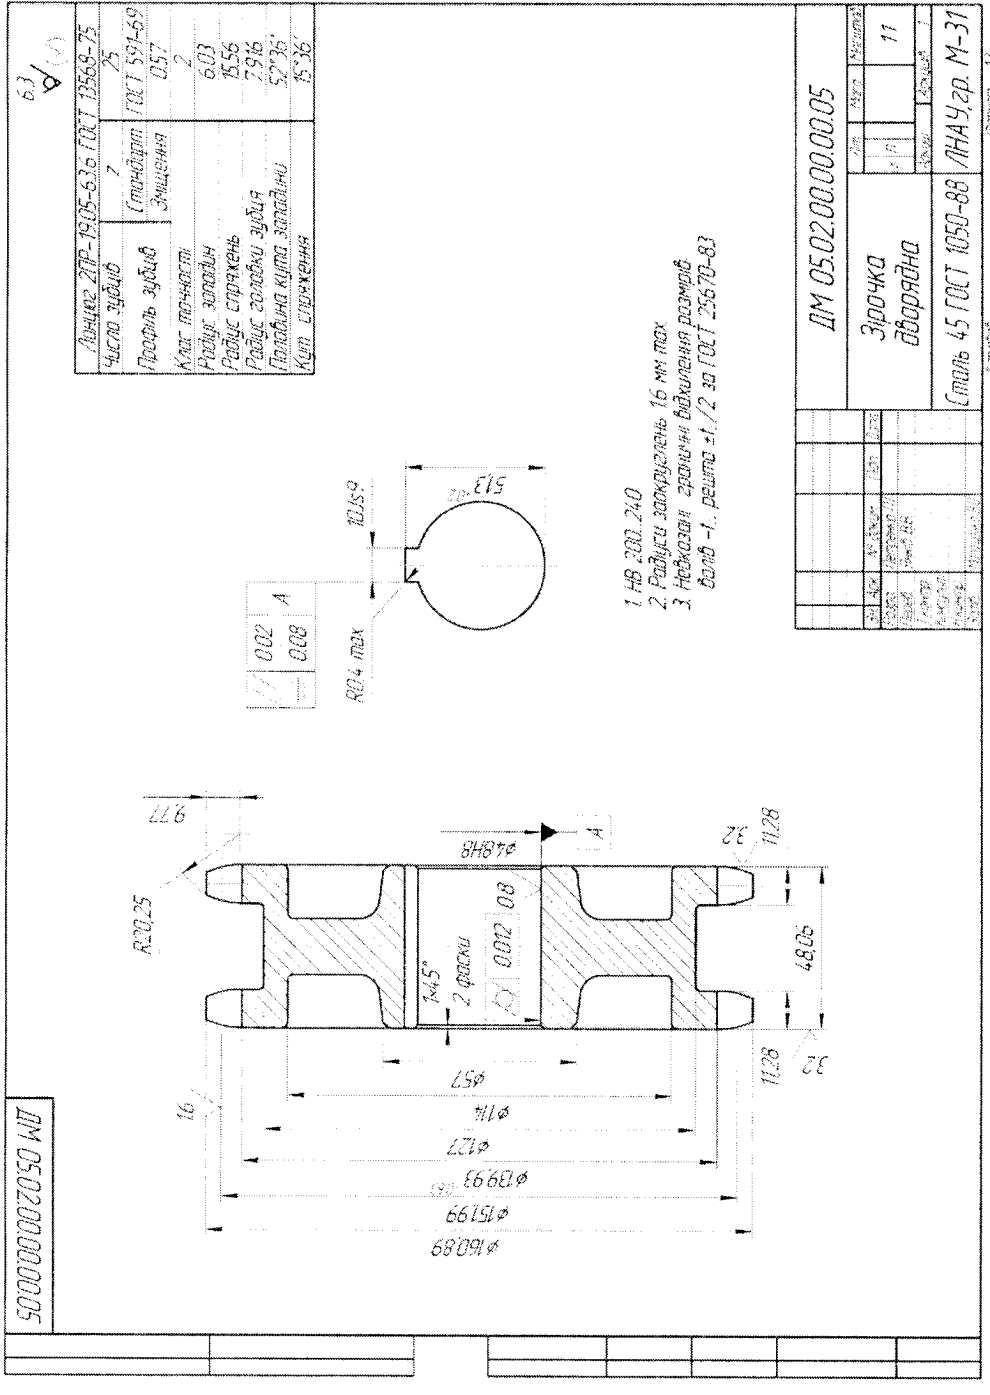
Приклад робочого креслення зірочки дворядної
